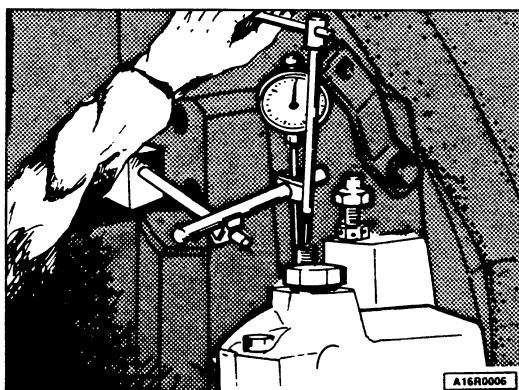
Puesta en fase del grupo regulador en el tractor.
